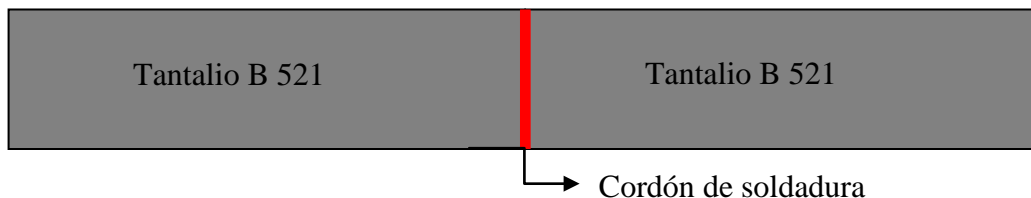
Preparación de las uniones para la soldadura.
